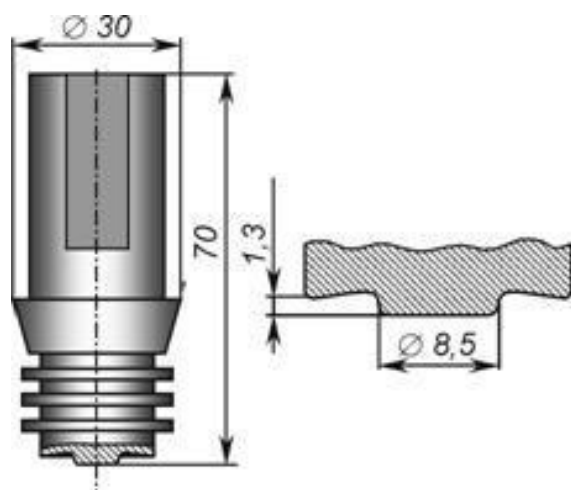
Параметры инструмента для сварки трением с перемешиванием
